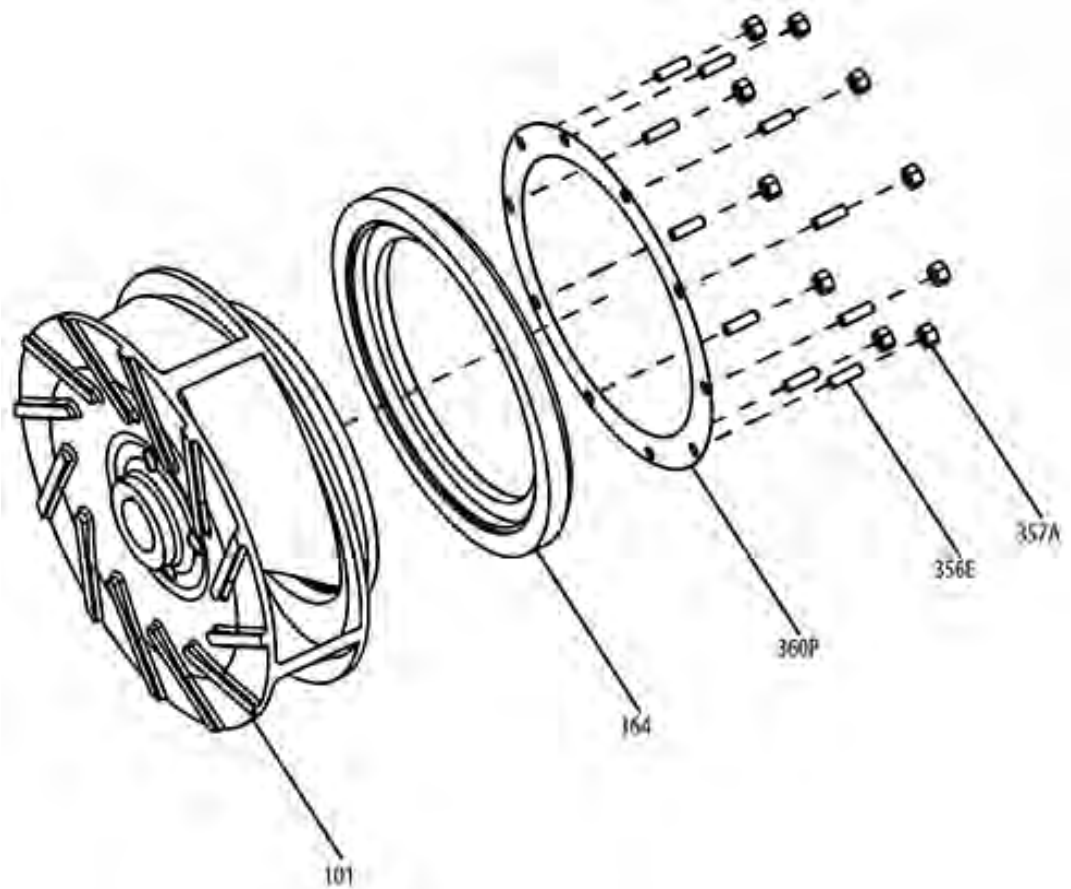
Explosionsansicht von 3180 und 3185 S, M, L, und XL Gruppen
